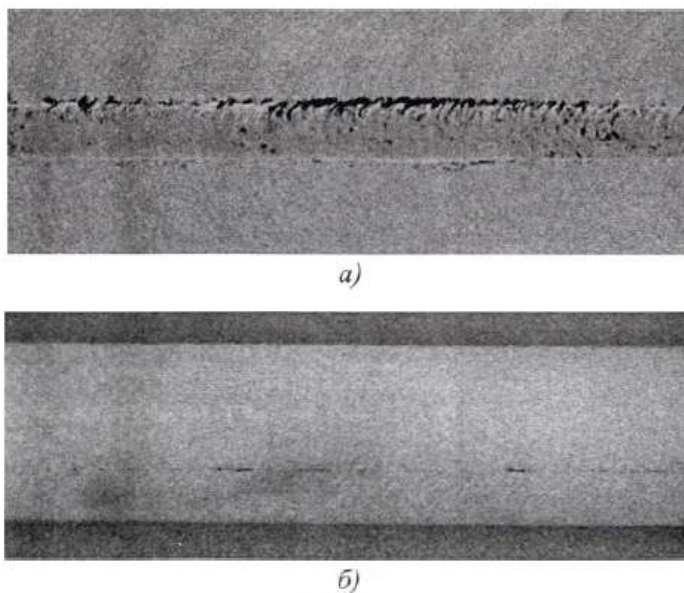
Рентгенограммы сварных швов СТП сплава 1565чМ [110]
